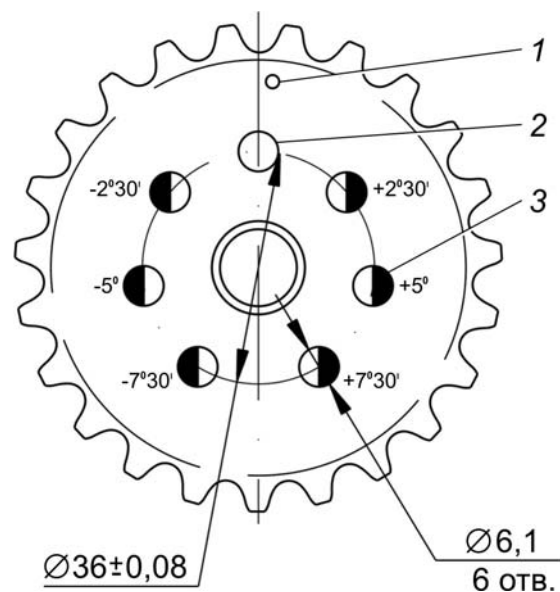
Звездочка распределительного вала с дополнительными отверстиями: 1 - метка; 2 - заводское отверстие; 3 - дополнительные отверстия.
